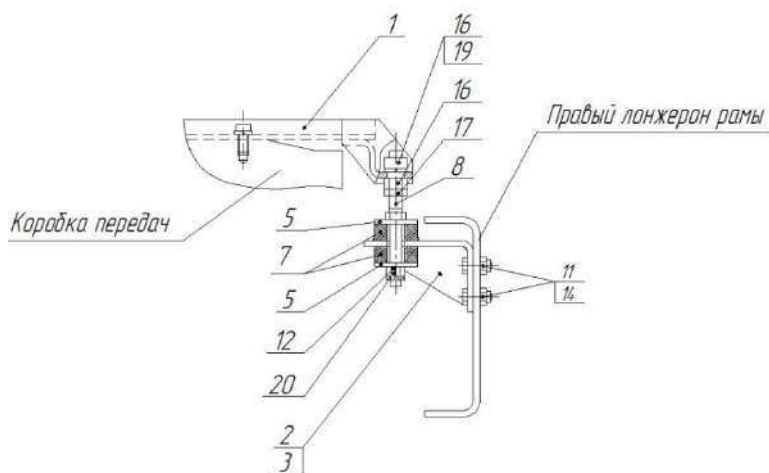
Схема установки дополнительной опоры коробки передач
